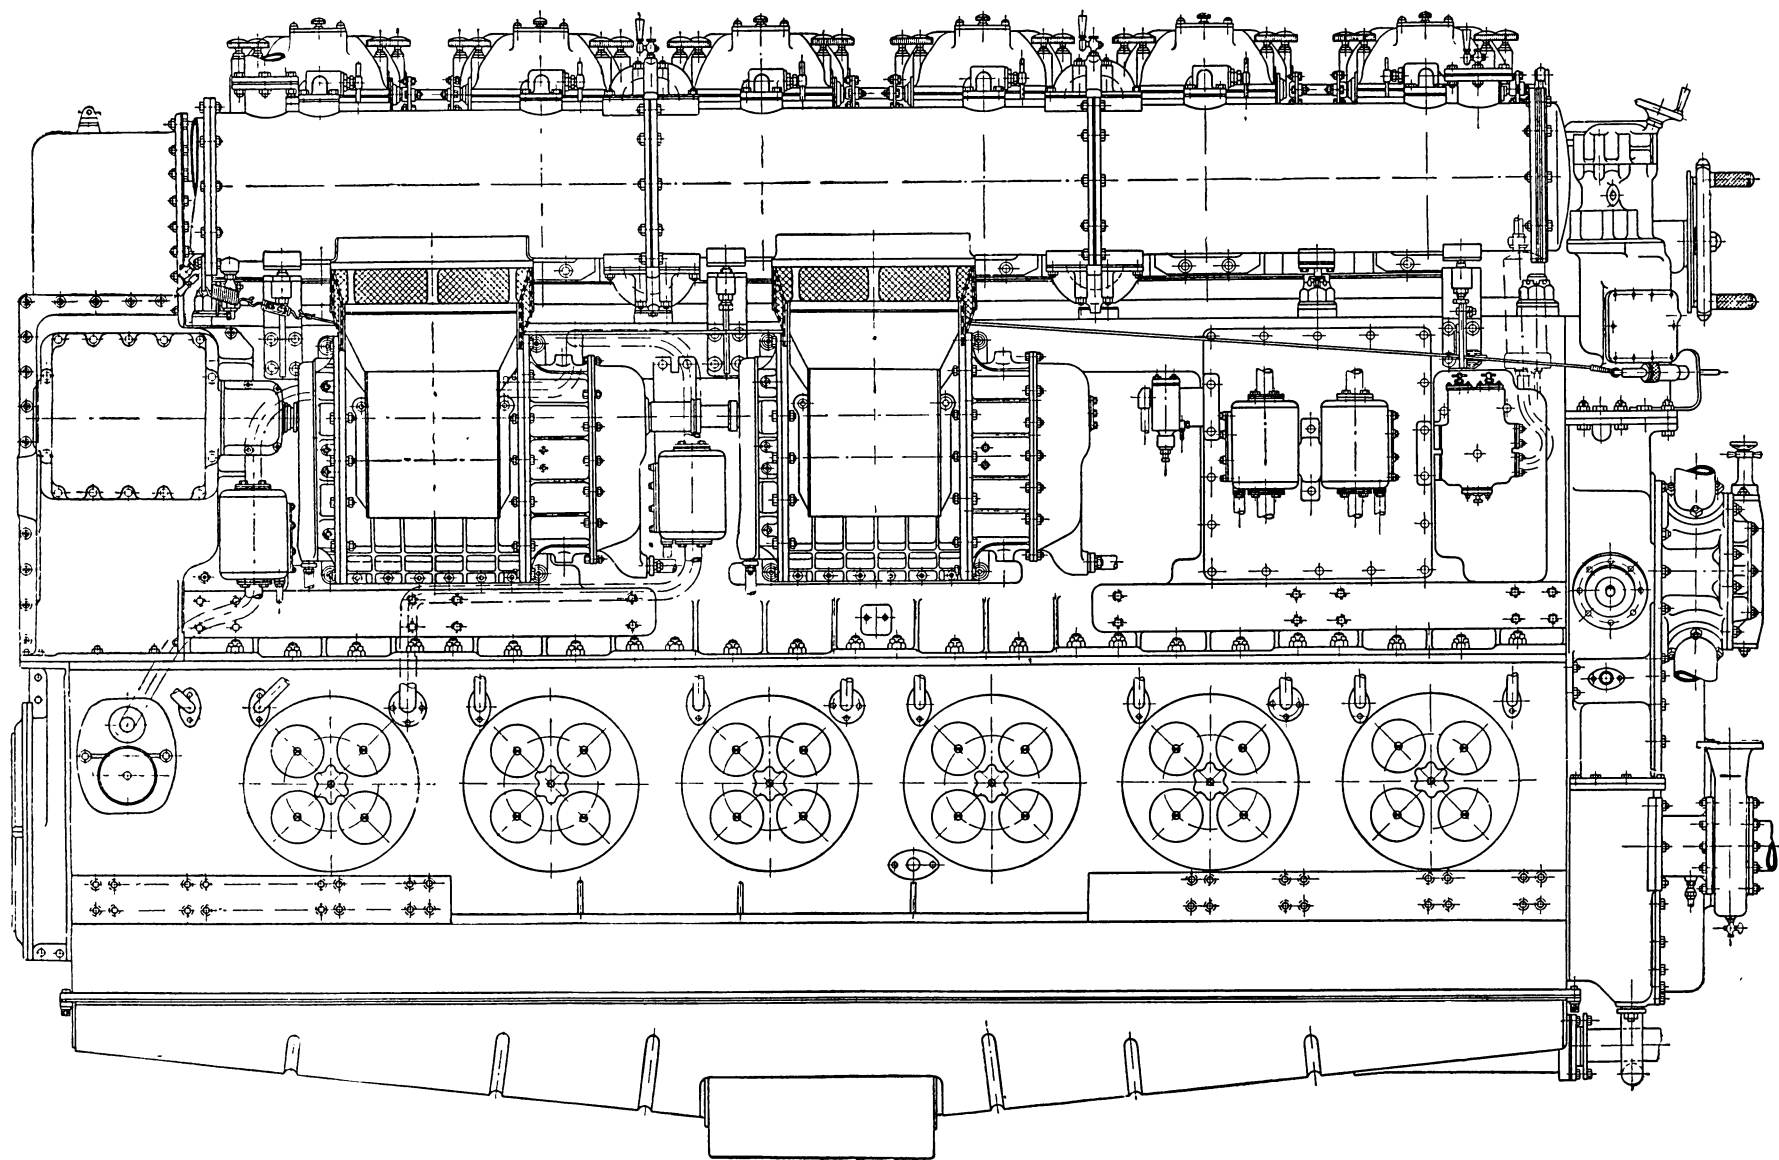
Общий вид двигателя со стороны выхлопного коллектора.
